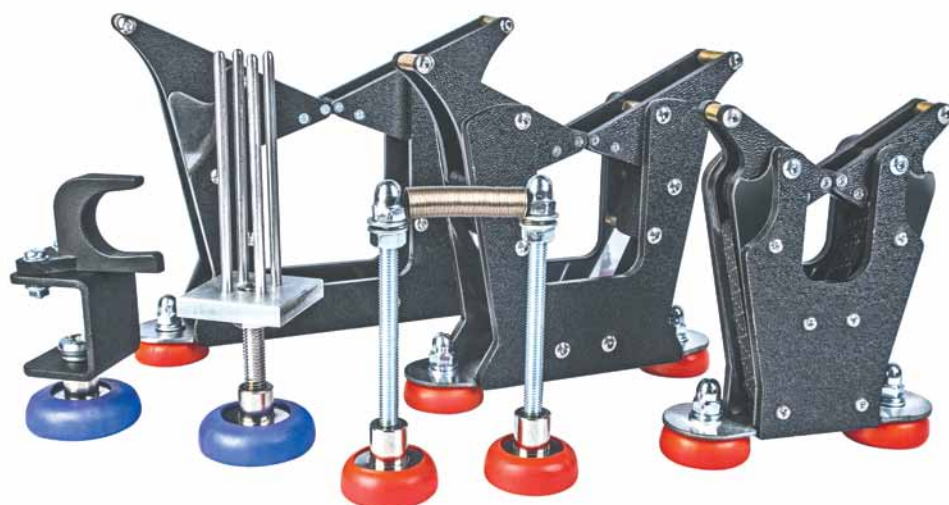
Магнитные держатели разного типа для сборочного плаза
